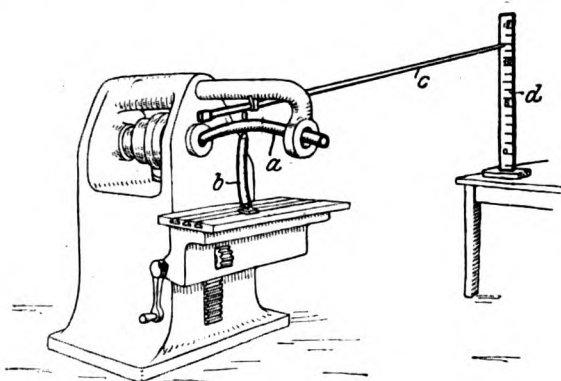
Fräsmaschine als Festigkeits-Prüfmaschine.
